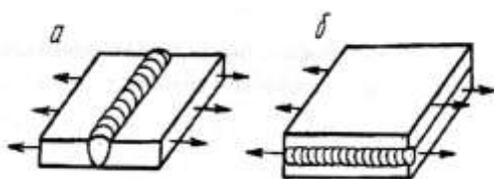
Сварные швы: а – рабочие, б – связующие
